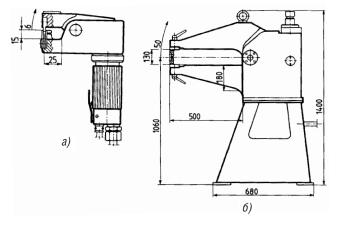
Оснащение для сборки а) ручной инструмент; б) стационарный пресс
